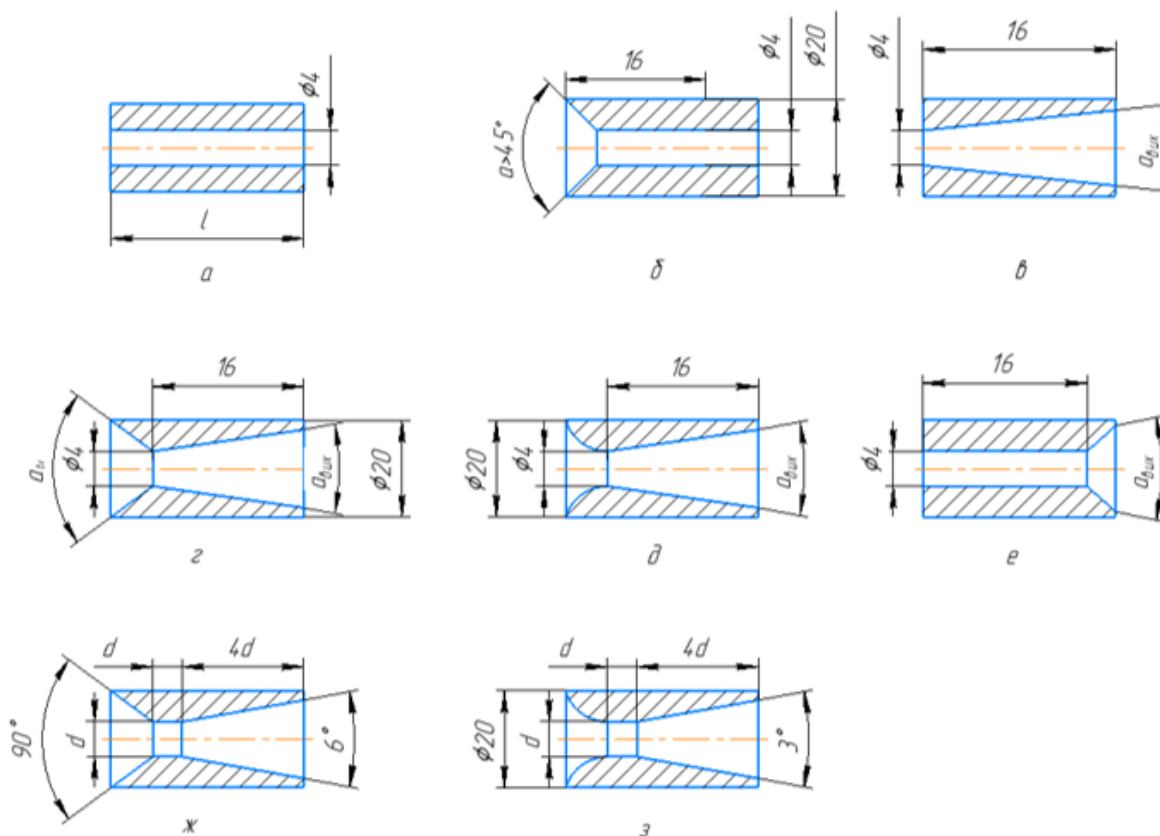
Конструкція основних типів насадків: а – циліндричний насадок; б – циліндричний насадок з конічним входом; в – конічний насадок, що розширюється; г – конічний насадок, що звужується та розширюється; д – коноїдально-конічний насадок; е – циліндричний насадок з конічним виходом; ж – конічний насадок, що звужується та розширюється з проміжною циліндричною частиною; з – коноїдально-конічний насадок з проміжною циліндричною частиною
